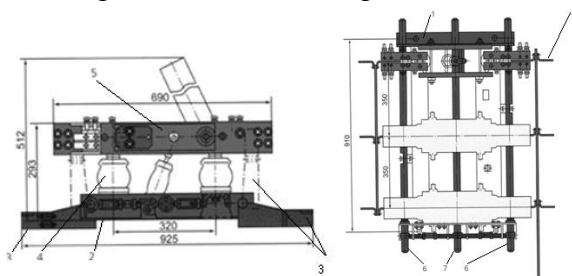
Разъединители рубящего типа для внутренней установки с двумя заземляющими ножами РВРЗ-2-10/2000 : 1 - рама; 2 - механическая блокировка основных и заземляющих ножей; 3 - заземляющий нож; 4 - опорный изолятор; 5 - главные ножи разъединителя; 6 - вал заземляющих ножей; 7 - вал главных ножей
